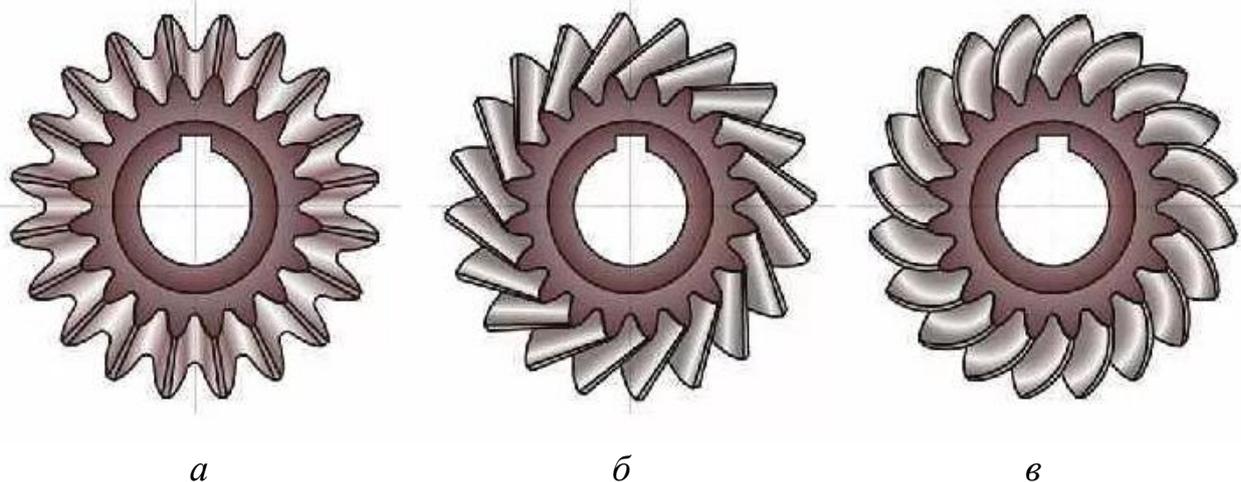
Виды конических зубчатых колес: а – с прямыми зубьями; б – с косыми зубьями; в – с криволинейными зубьями
